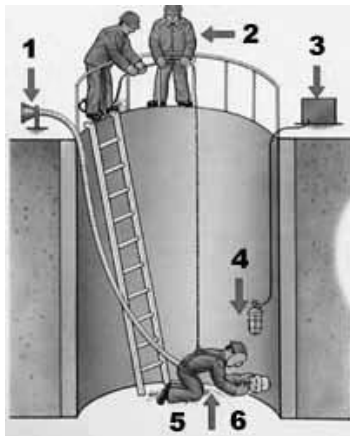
Сварочные работы внутри подземных сооружений:
